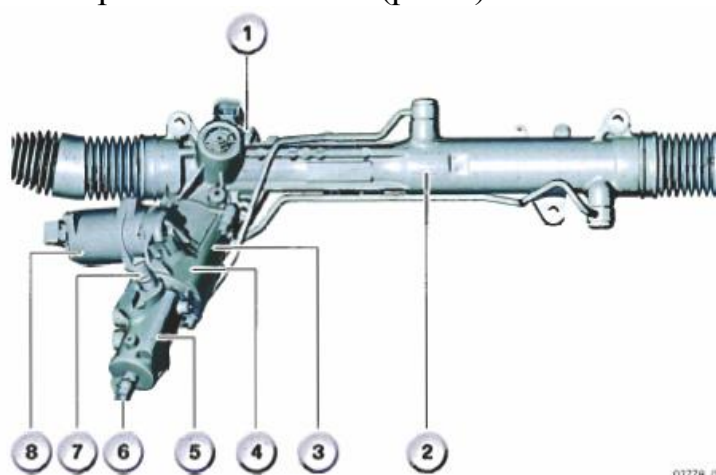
Рулевой механизм с зубчатой рейкой и исполнительным узлом активного рулевого исполнения: 1–датчик угла поворота; 2–реечное рулевое управление; 3–корпус планетарного механизма; 4–блокировка исполнительного узла активного рулевого управления; 5–клапан гидроусилителя; 6–вал рулевого управления; 7–датчик температуры жидкости для гидравлических систем; 8–электродвигатель.
